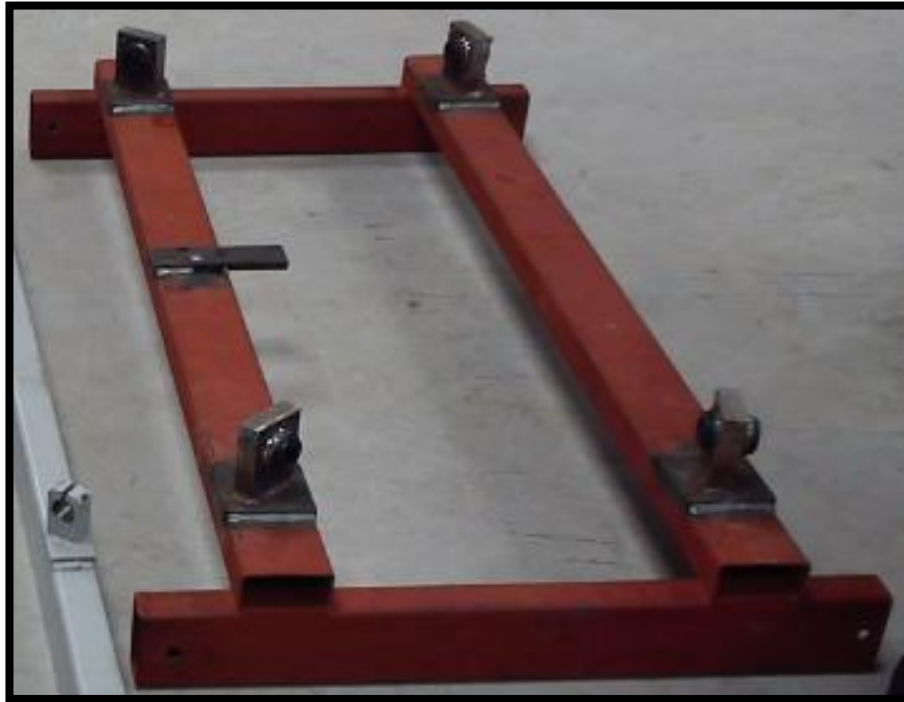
Ubicación y soldadura de Alojamiento rotula-rodamiento y de la placa bastidor-motor.
